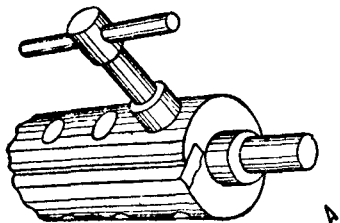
Крепление ножей фугочного станка торцевым ключом.
